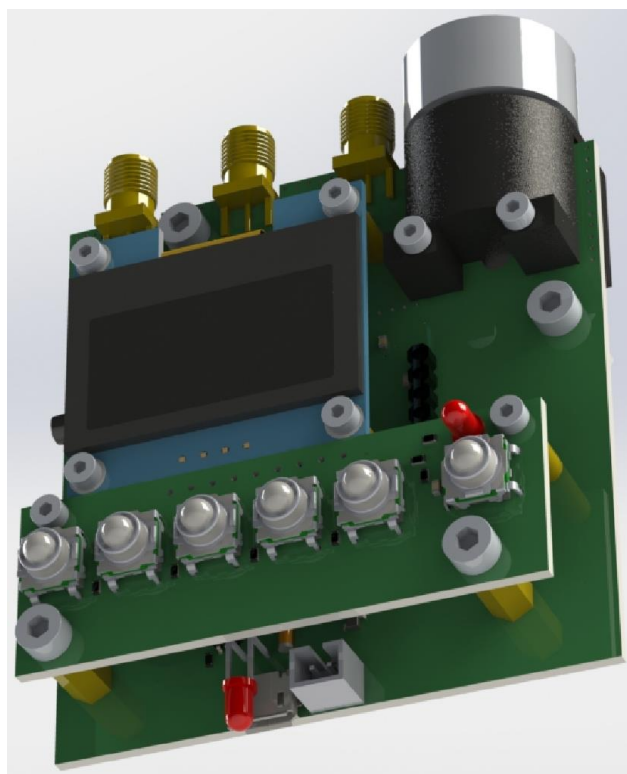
Загальний вигляд пристрою у вікні редактора Multi-board Assembly
